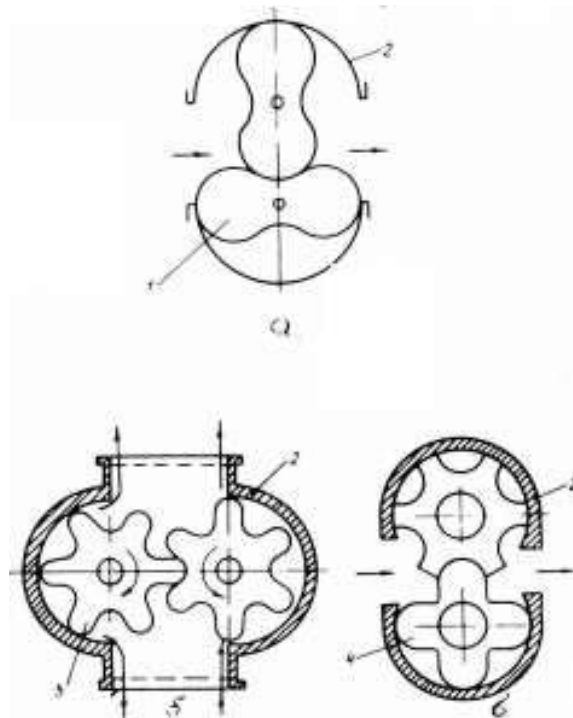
Схеми двороторних вакуумних насосів (РУТС): а) типу РУТС; б) шестеренчатого; в) гвинтового; 1 – ротор; 2 – корпус; 3 – гвинт; 4 – шестерня.
